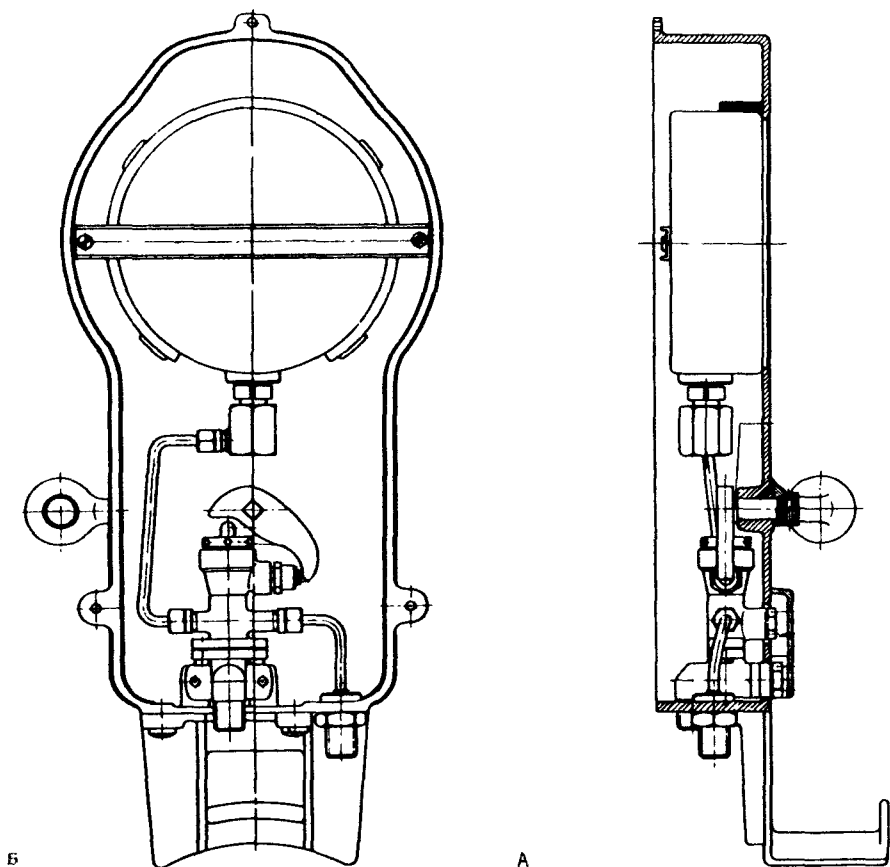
Внутренний вид манометра для шин: а — чертеж показывает вид устройства сзади и сбоку. Опытный ретушер легко представляет пространственное и пластическое изображение деталей устройства; б — конструкторская ретушь по рисунку: пластический рисунок выглядит, как фотография
